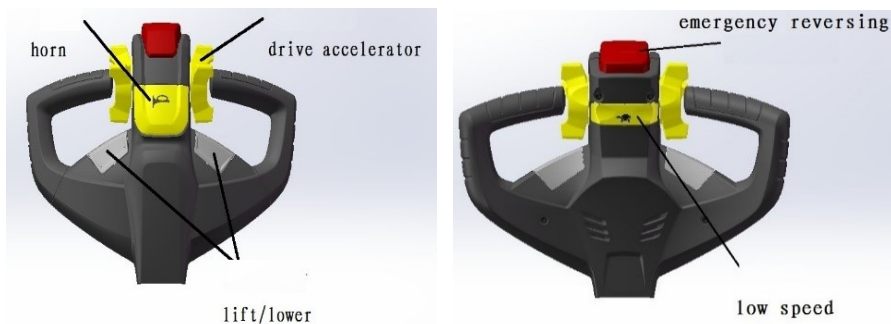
Horn – звуковой сигнал; lift/lower – кнопки управления «вверх»/«вниз»; drive acceleration – высокая скорость; emergency reversing – кнопка аварийного обратного движения; low speed – медленная скорость.
